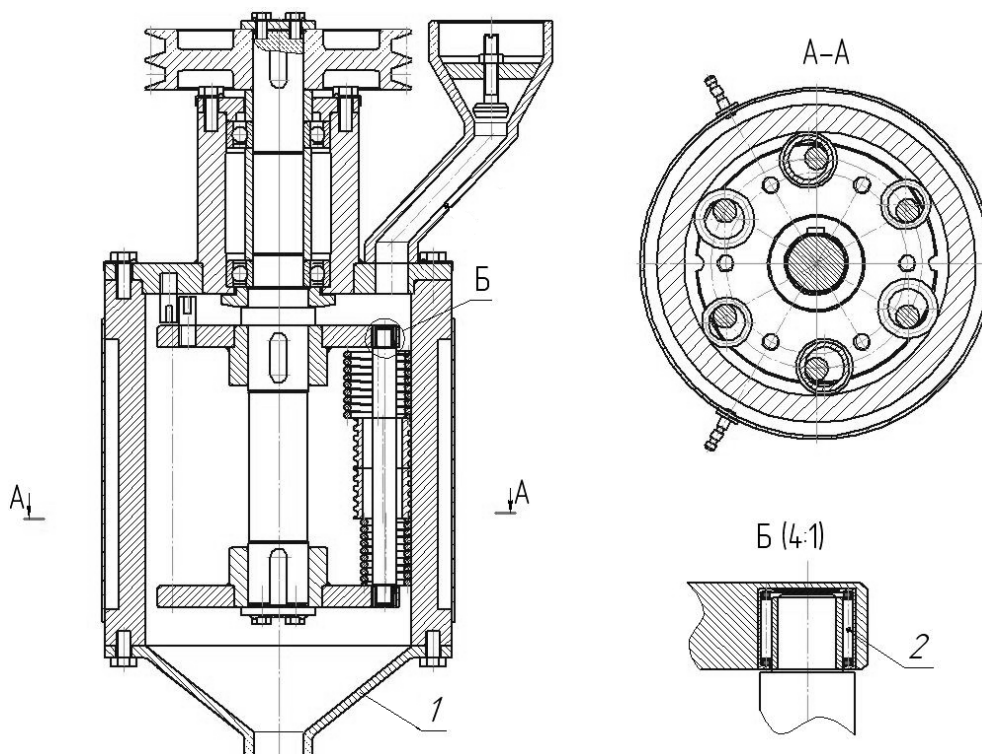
Модернизированная конструкция роторной головки ролико-кольцевой мельницы RTM4: 1 – фланец; 2 – роликовый радиальный игольчатый однорядный подшипник
